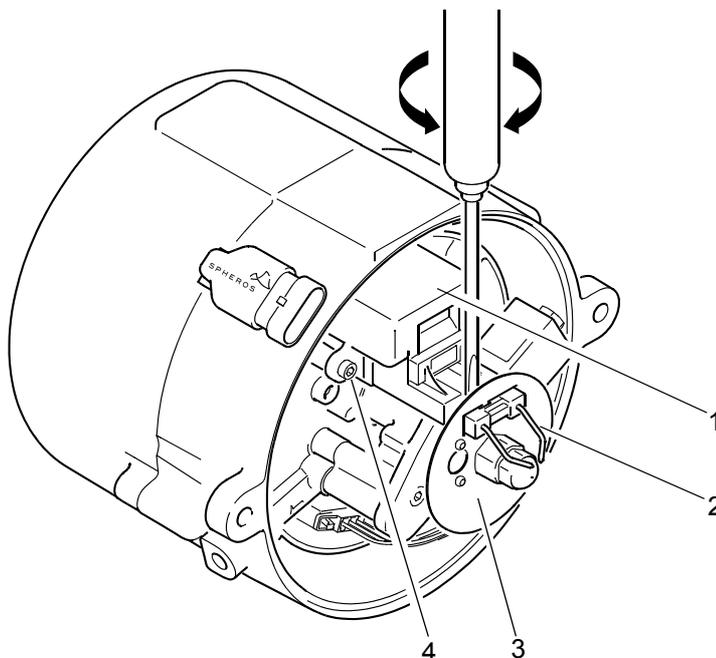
Smontaggio del trasduttore scintilla di accensione / dell'elettrodo di accensione
